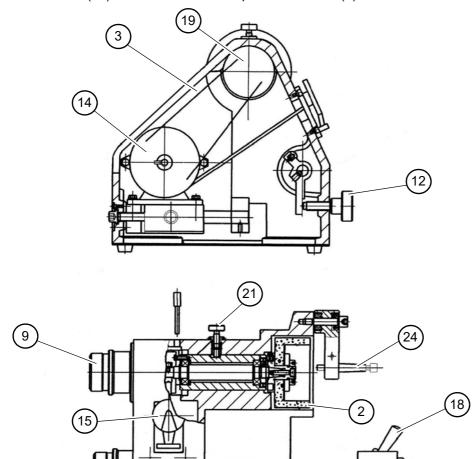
Stichel- und Werkzeugschleifmaschine
